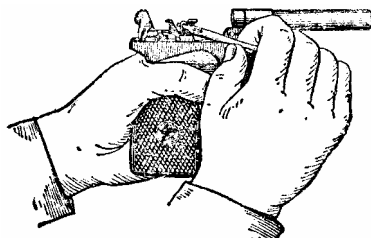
Снятие крючка пружины шептала с затворной задержки.
